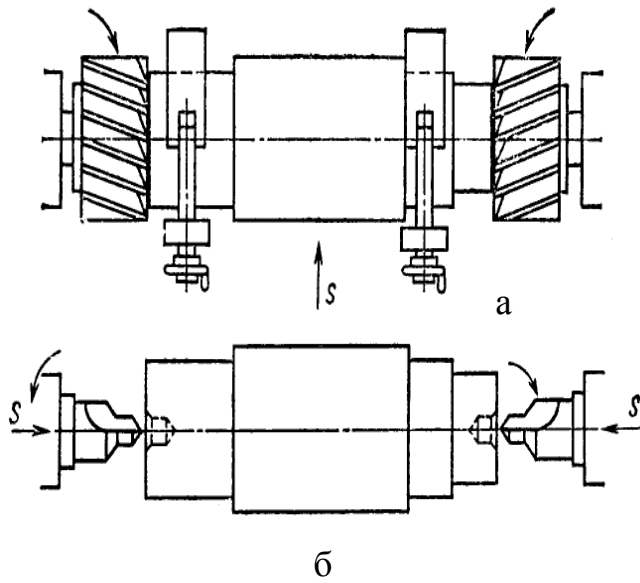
Схема обробки на фрезерно-центрувальному верстаті.
